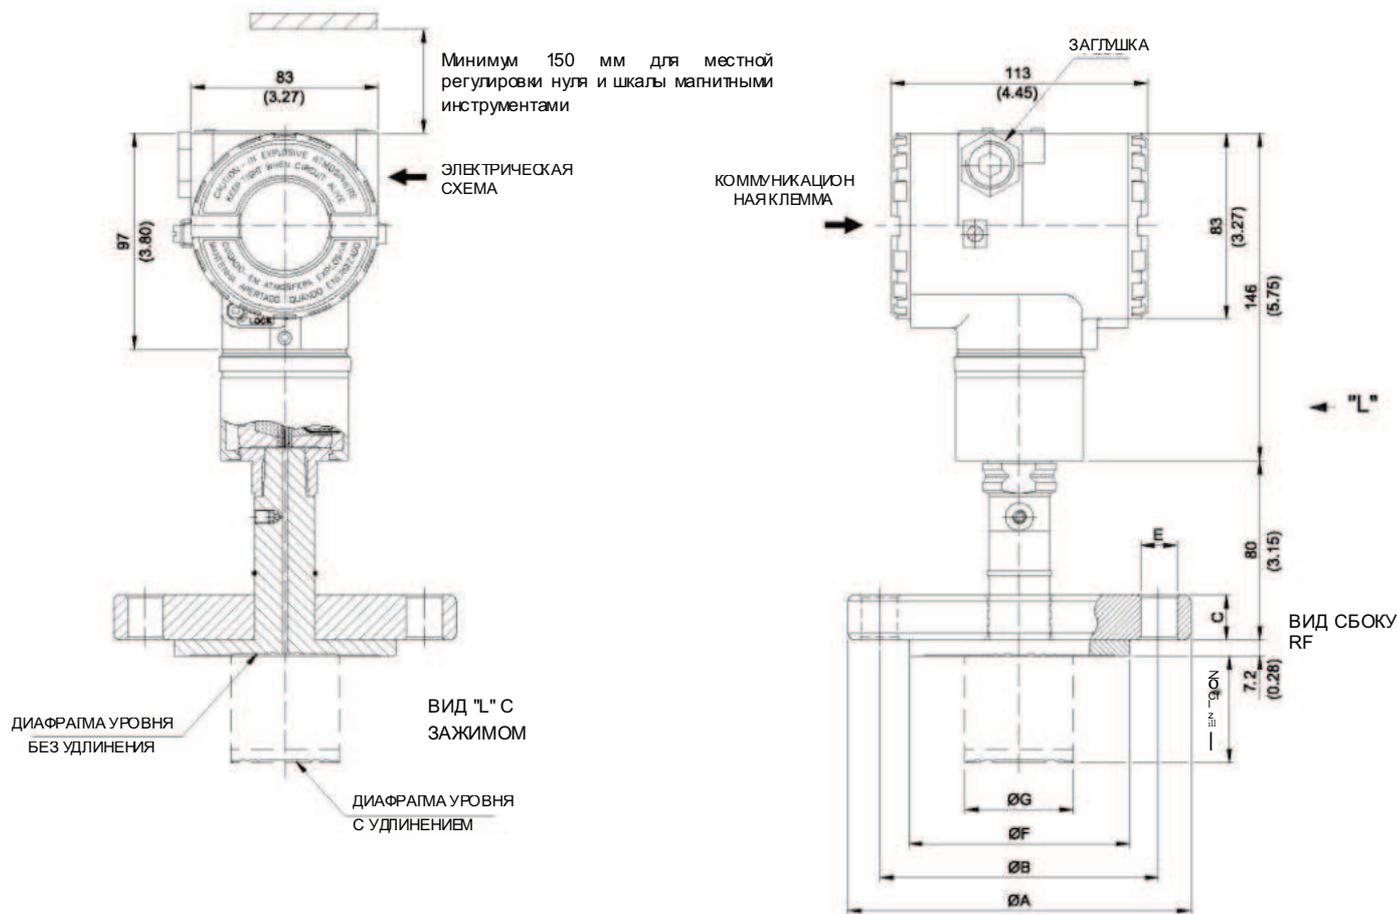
(b) - Размерный чертёж и положения установки для LD290 - Санитарный
